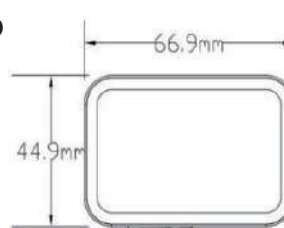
YL61F-F Dibujo de las dimensiones de la vista frontal del instrumento
